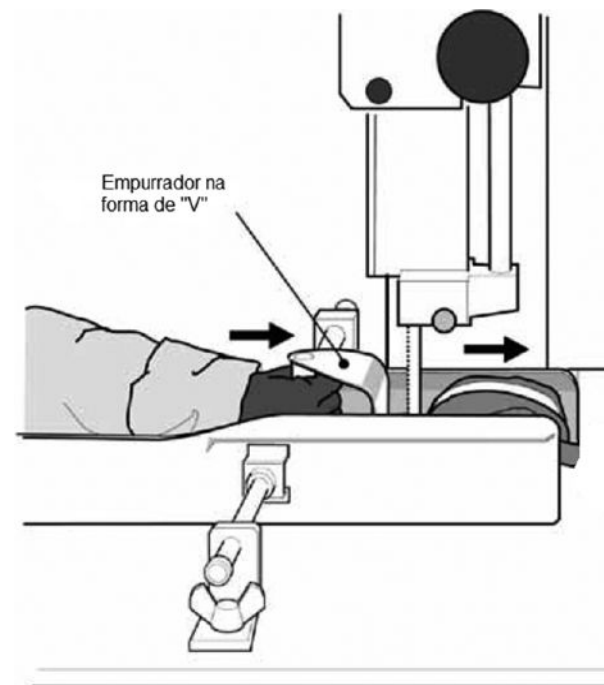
Exemplo de dispositivo para proteção da mão do trabalhador
